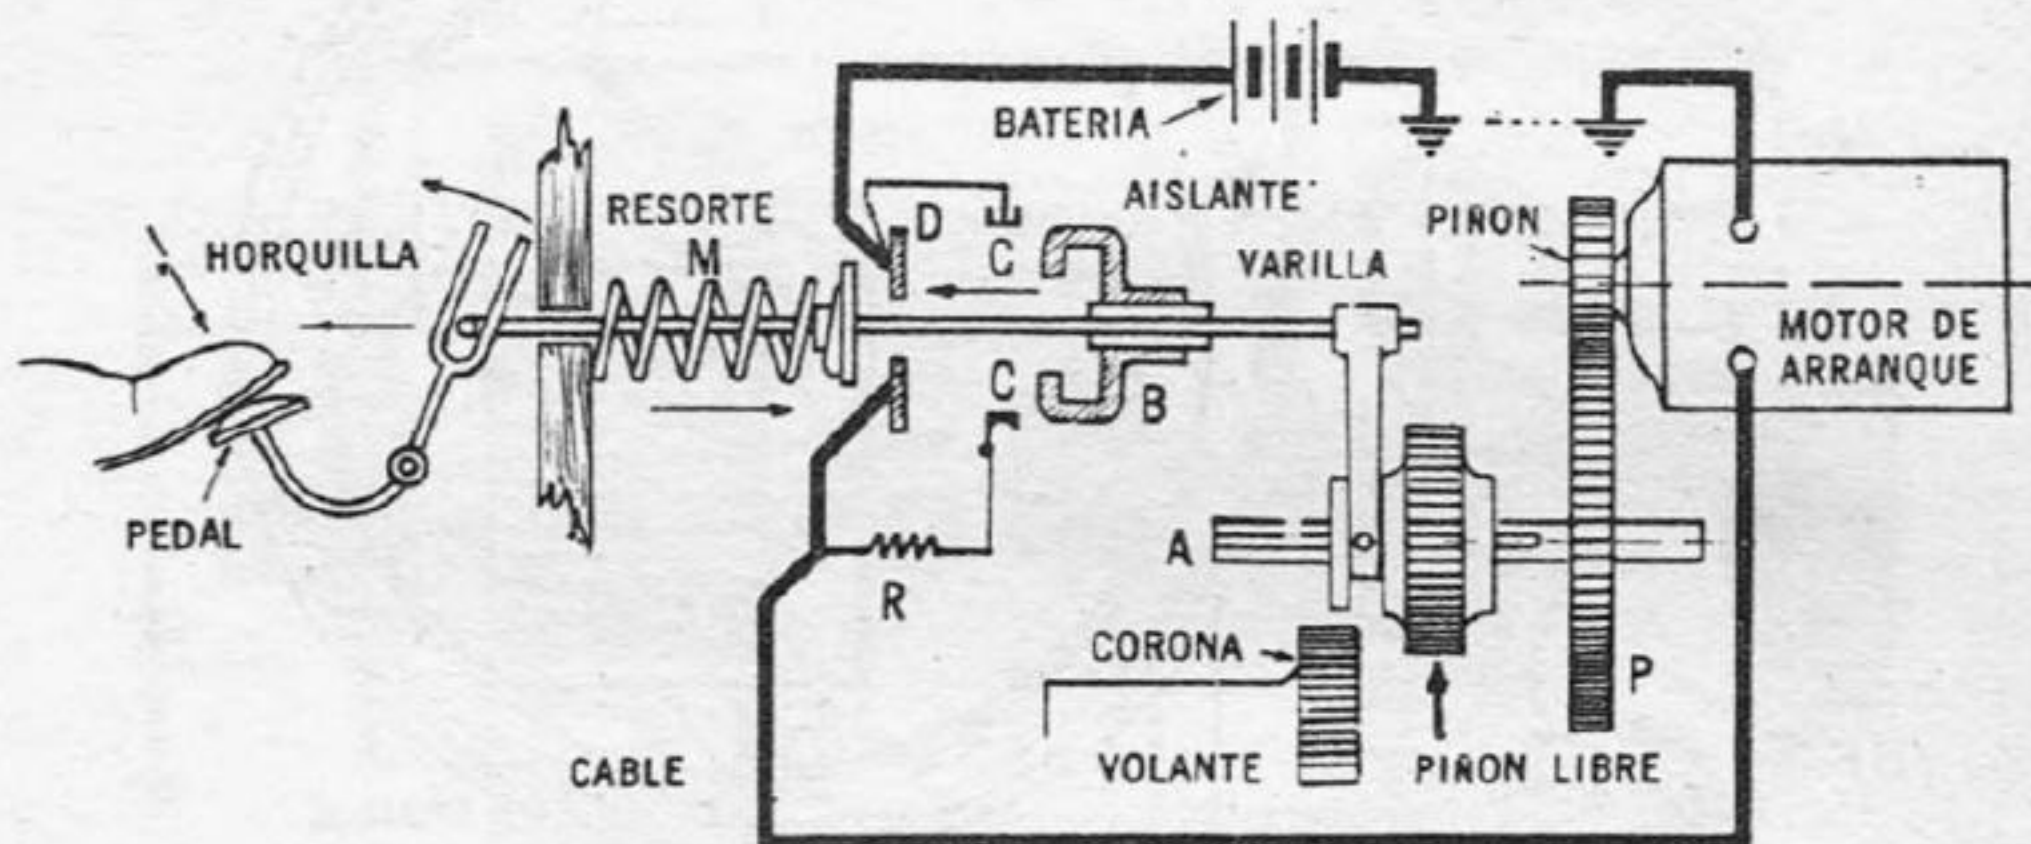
Acoplo mecánico simple entre el motor de arranque y el de explosión.
